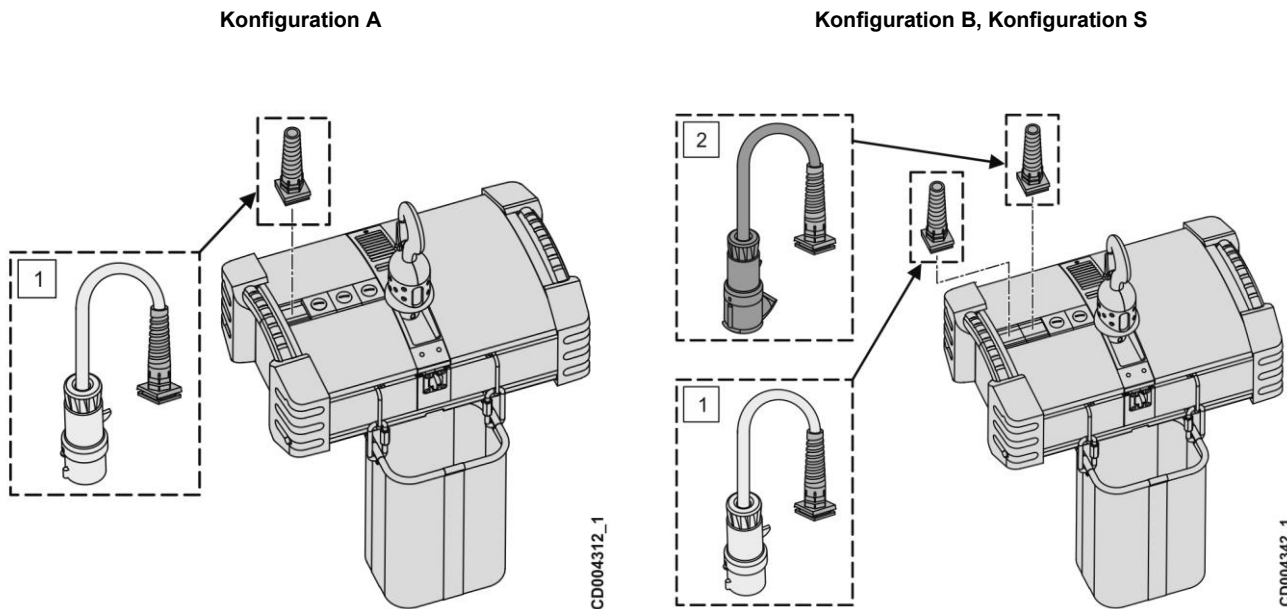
Beispiel für Kabeleingänge für Hubwerks-Stromversorgung und -Steuerung
